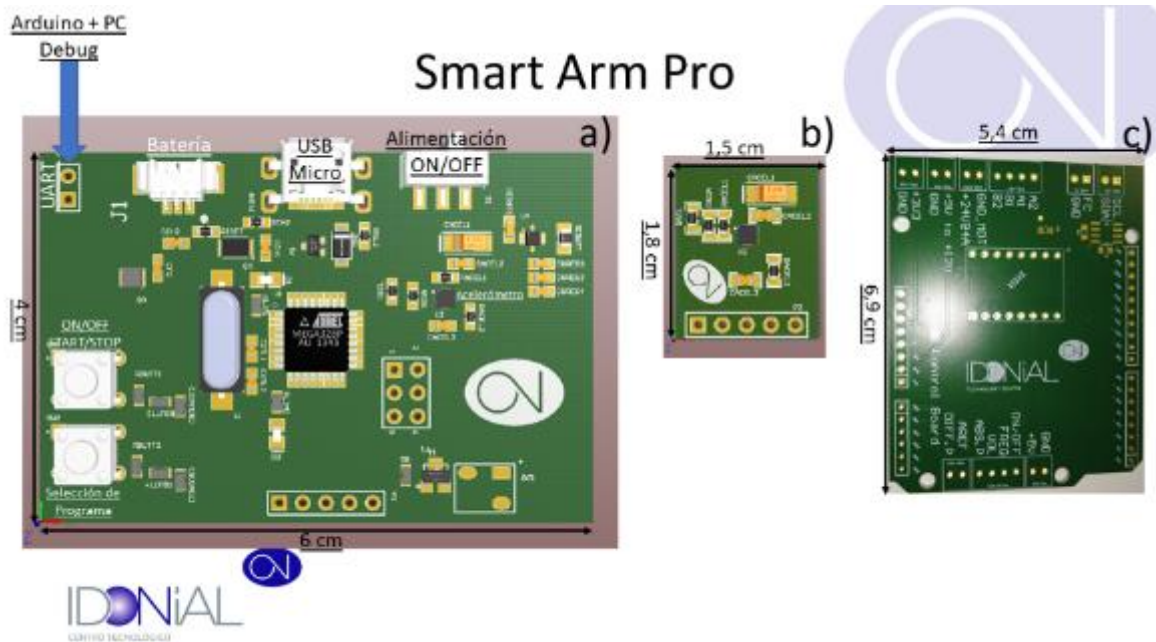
PCBs diseñadas para el dispositivo SMART ARM PRO, a) Placa de control, b) Placa auxiliar y c) Placa de control del motor paso a paso.
